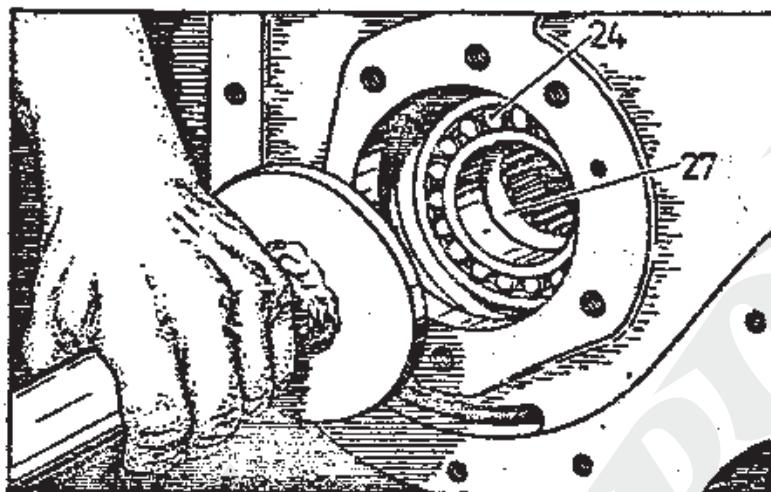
Вдавливание бочкообразного роликоподшипника 24 в гнездо зубчатого колеса 27 посаженного в корпусе.
